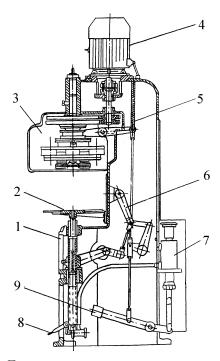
Полуавтоматическая закаточная машина СЗК М: 1 — станина; 2 — нижний патрон; 3 — закаточная головка; 4 — электродвигатель; 5 — пружина; 6 — рычажная система; 7 — пневмоцилиндр; 8 — педаль пневматического включения машины; 9 — педаль механического включения машины
